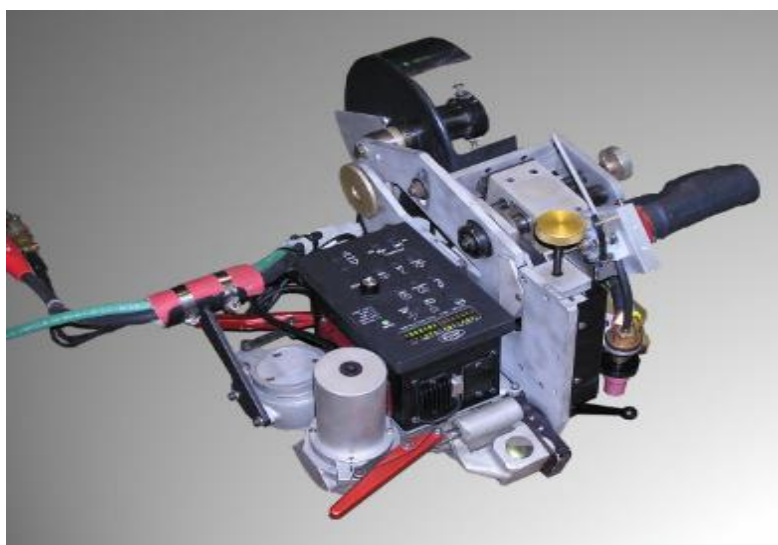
Внешний вид сварочной головки М-300-С
